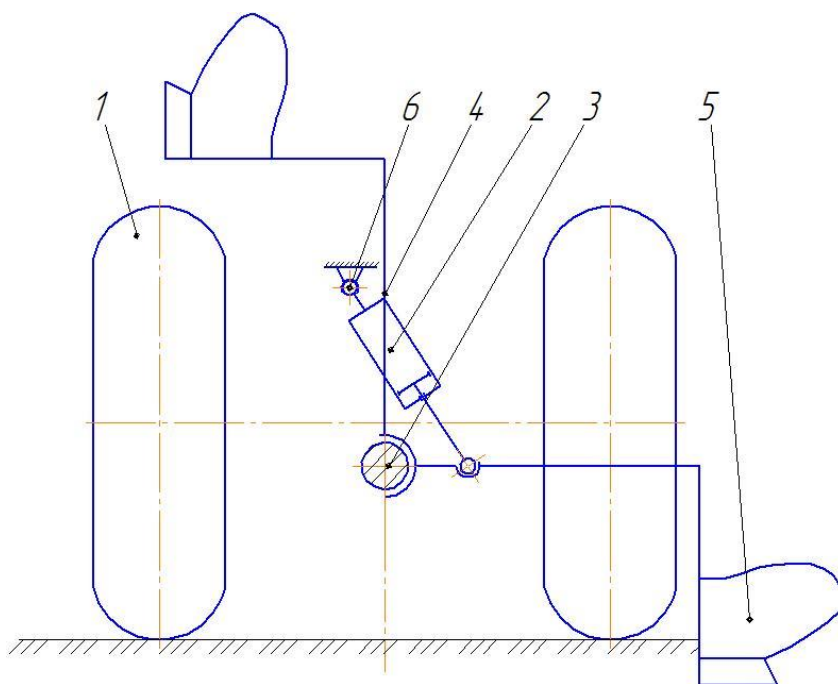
Механізм повороту плуга «IBUS»: 1 – тракторне колесо; 2 – гідроциліндр; 3 – рама; 4 – рама кріплення корпусу плуга; 5 – корпус плуга; 6 – тракторна підвіска.
